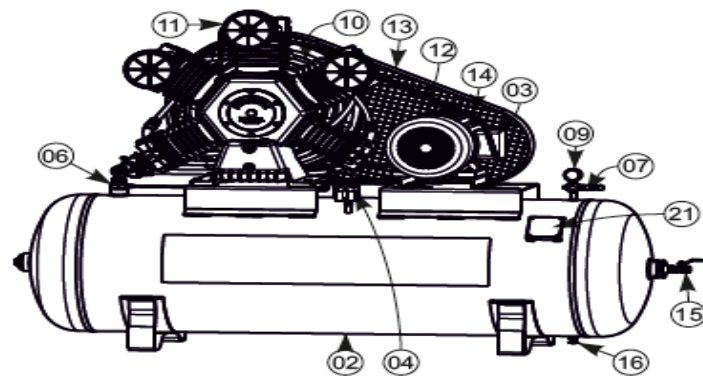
Partes que componen un Compresor Alternativo Lubricado
